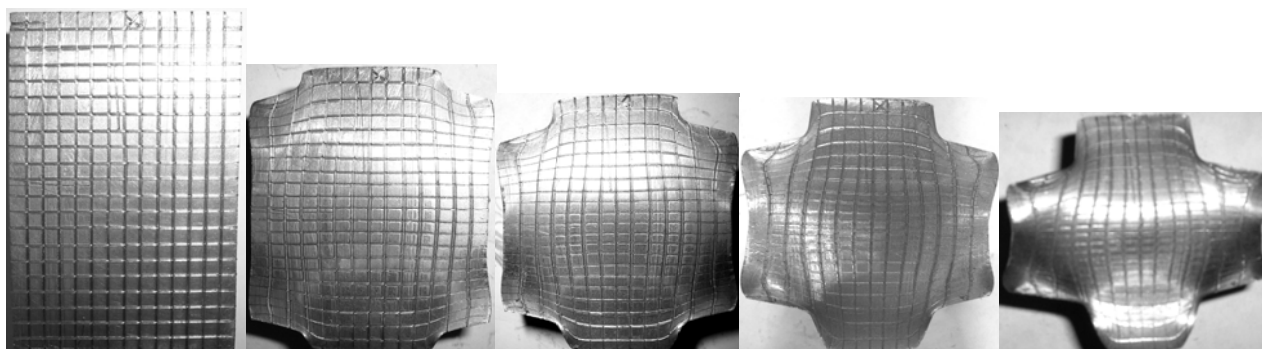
Поэтапное изменение формы заготовки и координатной сетки
